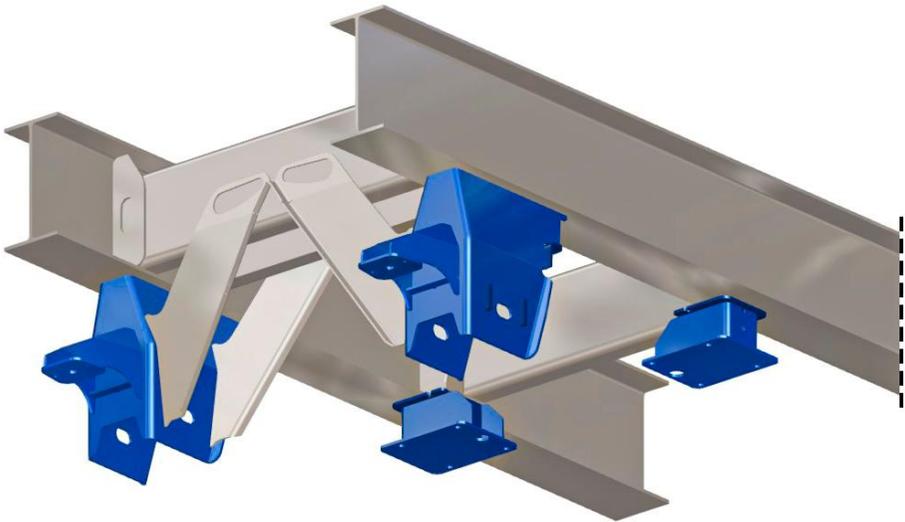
Reforço de ligação da travessa e suporte frontal – AirSteer
